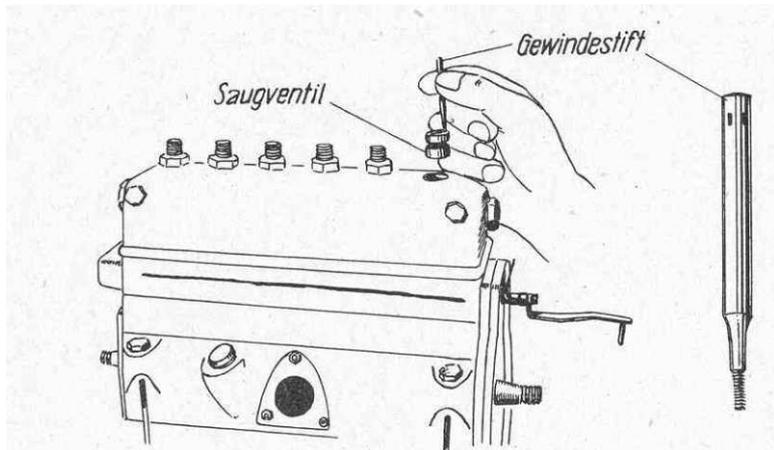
Ein Saugventil wird aus dem Pumpenoberteil gehoben
